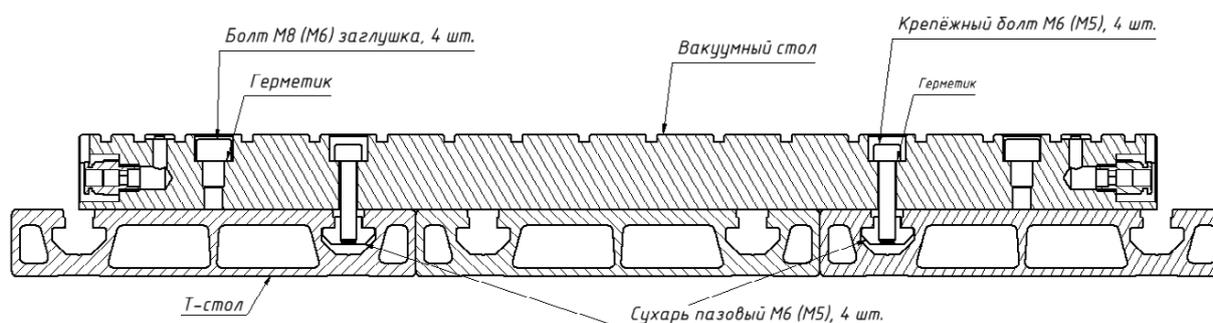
Сборочный чертёж монтажа вакуумной секции с помощью крепежных отверстий
